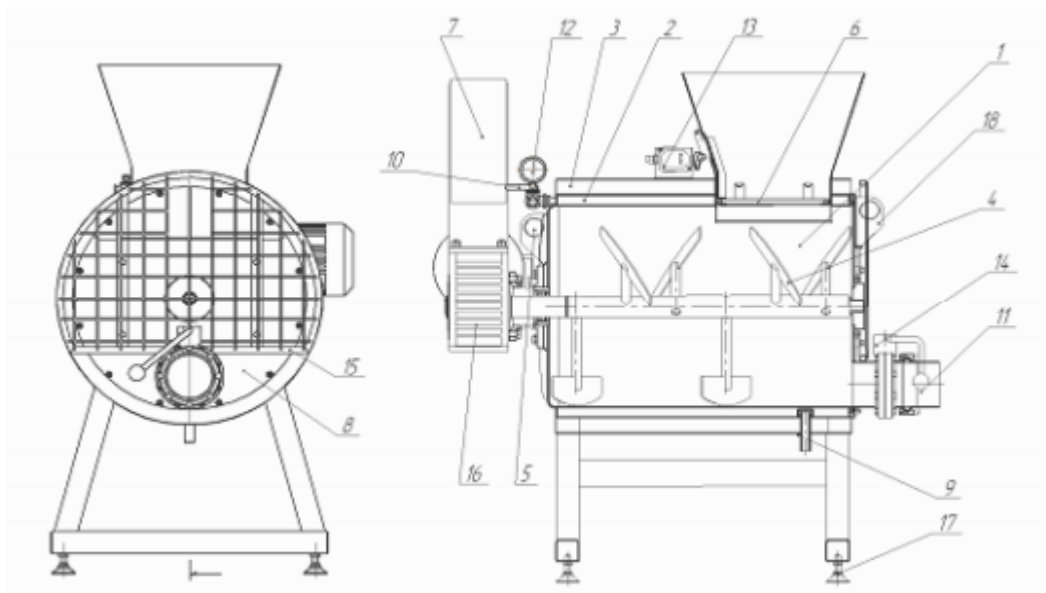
Машина для плавлення сирної маси: 1 – корпус внутрішній; 2 – рубашка підігріву; 3 – кожух захисний; 4 – мішалка; 5 – біметалевий термометр; 6 – кришка; 7 – магнітний пускач; 8 – фланець; 9 – патрубок зливу конденсату; 10 – вентиль подачі пари; 11 – злив; 12 – манометр; 13 – вимикач кінцевий; 14 – затвор дисковий; 15 – захисна огорожа; 16 – мотор-редуктор; 17 – гвинтові опори; 18 – вантажопідійомна петля.
